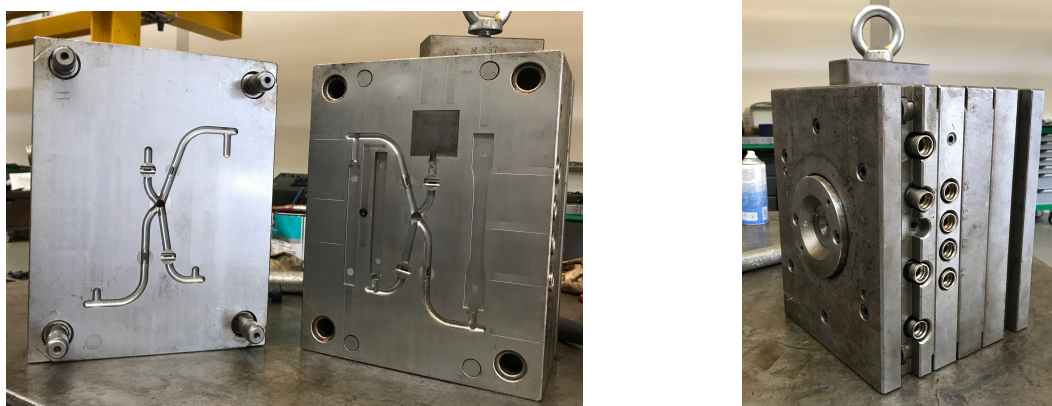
Molde utilizado para a produção dos provetes e das placas.
